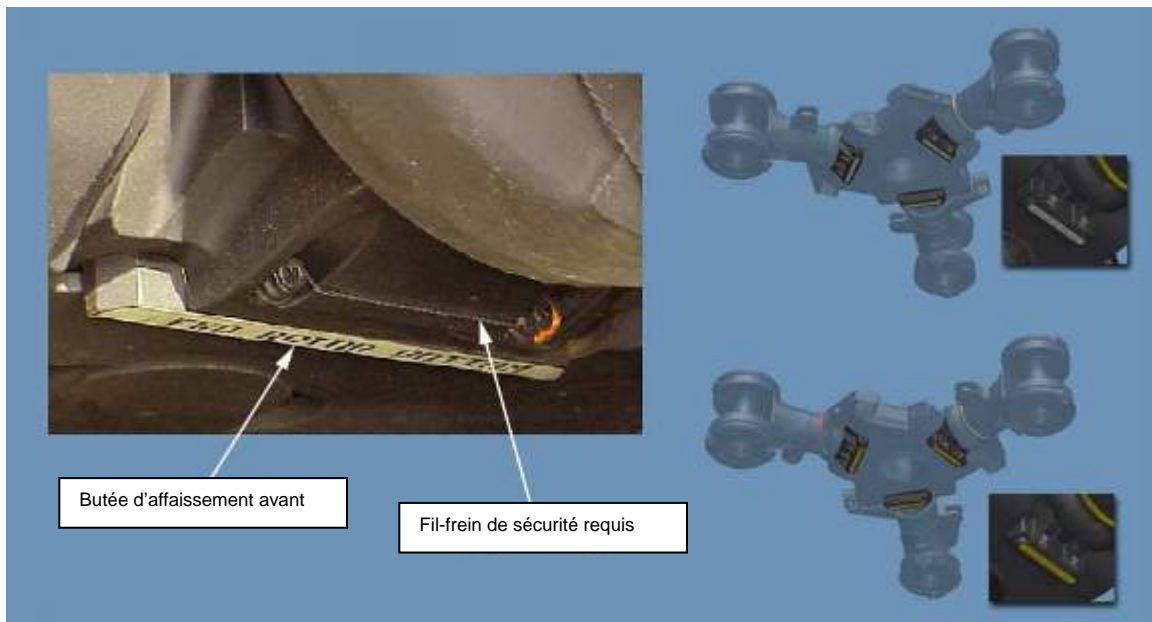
Ensemble de butées d'affaissement avant et arrière
